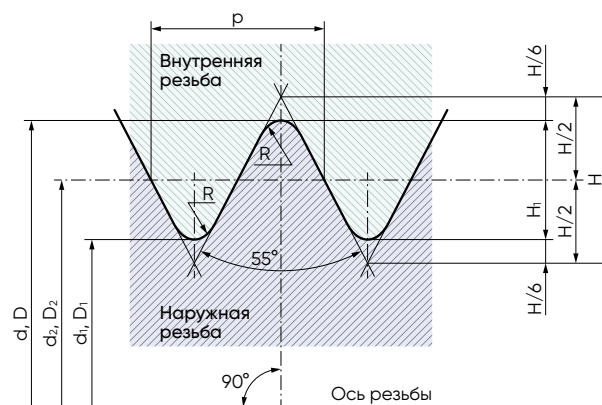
Параметры цилиндрической резьбы Уитворта
